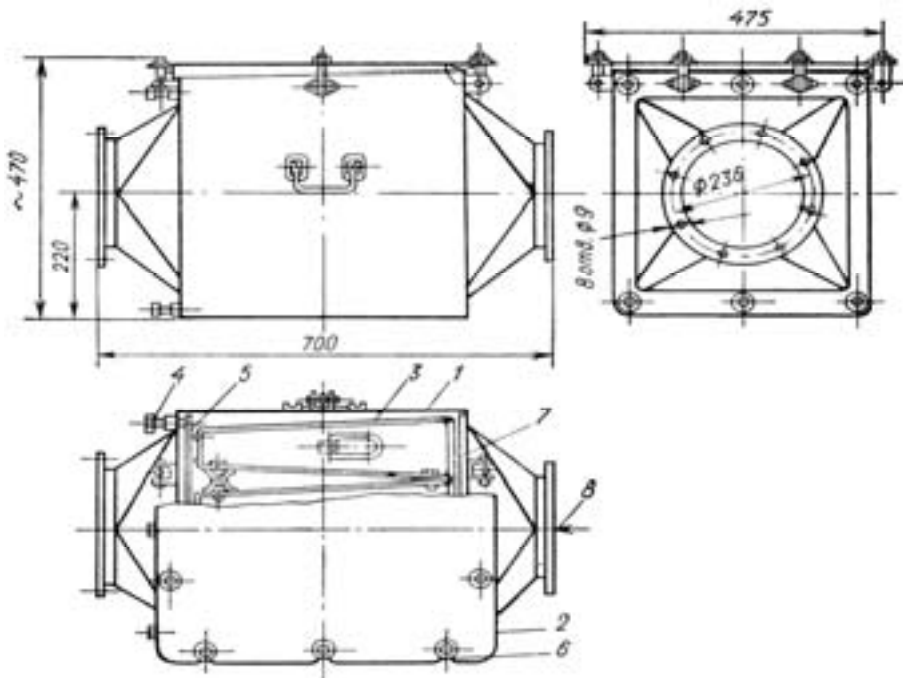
Передфільтр ПФП-1000: 1 – корпус; 2 – кришка корпуса;
